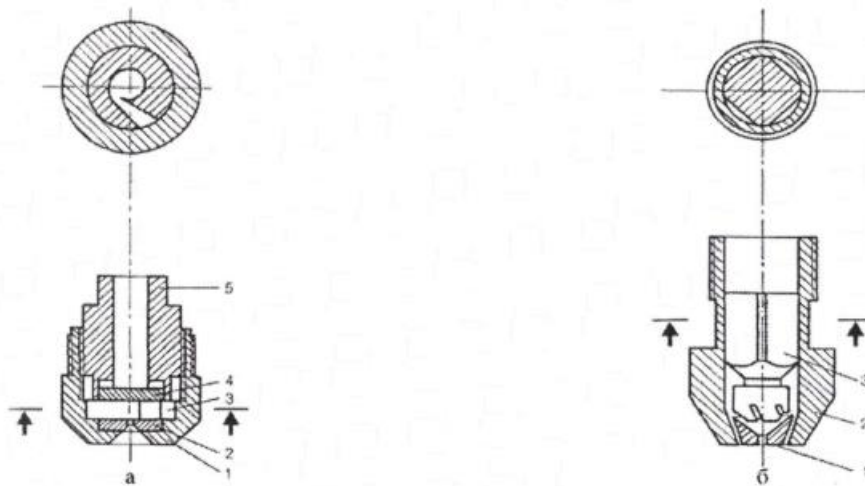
Механічні відцентрові форсунки: а - з тангенціальним завихрителем: 1 - зовнішній корпус; 2 - сопло; 3 - тангенціальний завихритель; 4 - шайба; 5 - внутрішній корпус; б - з повнотілою щілинним завихрителем: 1 - сопло; 2 - корпус; 3 - завихрювач.
